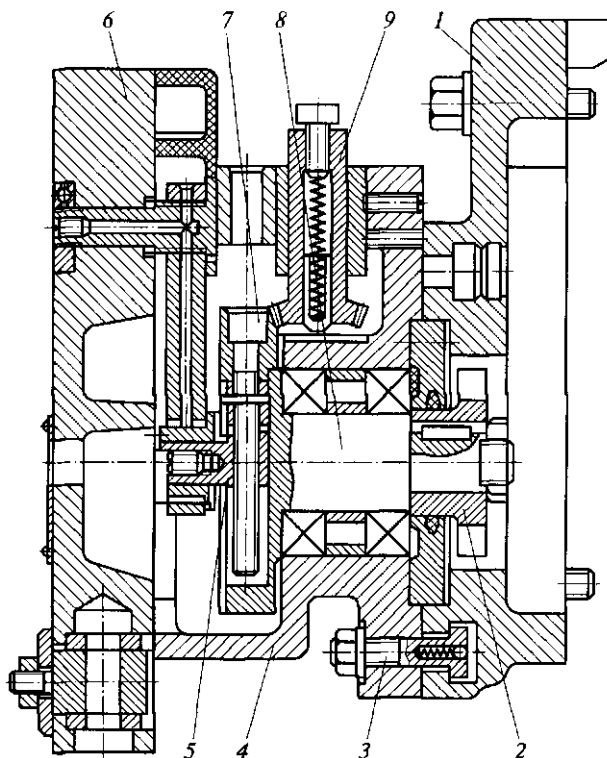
Долбежная головка комбинированного фрезерно-долбежного станка:
